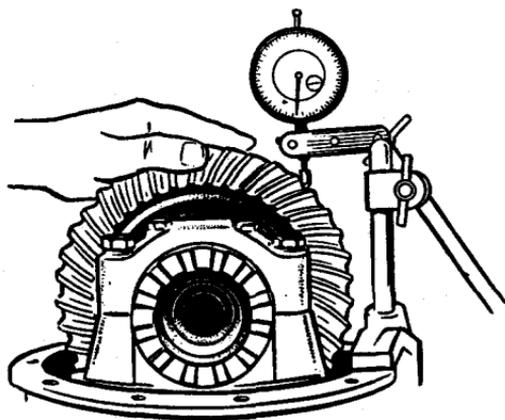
Замер бокового зазора в зацеплении главной передачи с помощью индикатора.
